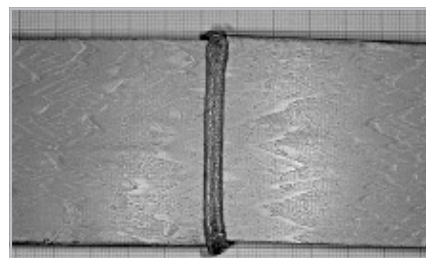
Сварной шов плоского листового образца из РЕИ, полученного при сварке нагретым инструментом встык
